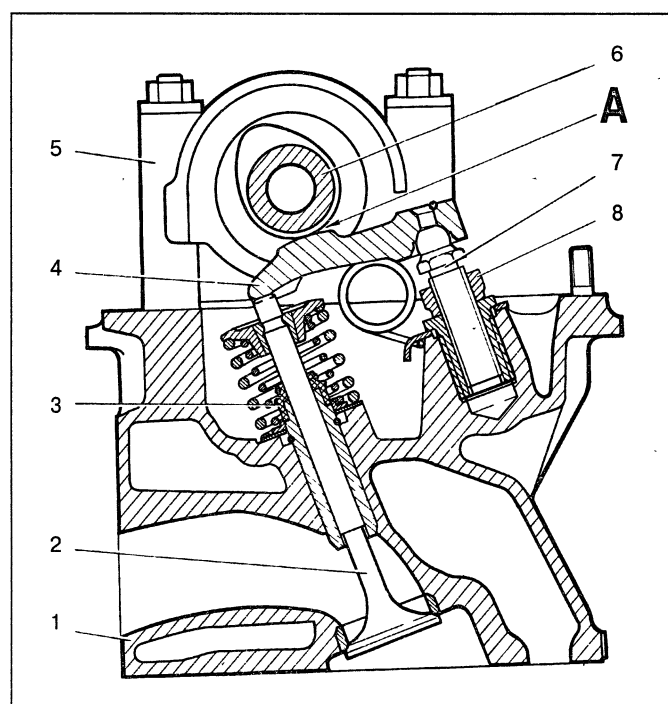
Разрез головки цилиндров по выпускному клапану: 1 – головка цилиндров; 2 – клапан; 3 – маслоотражательный колпачок; 4 – рычаг клапана; 5 – корпус подшипников распределительного вала; 6 – распределительный вал; 7 – регулировочный болт; 8 – контргайка регулировочного болта; А – зазор между рычагом и кулачком распределительного вала
